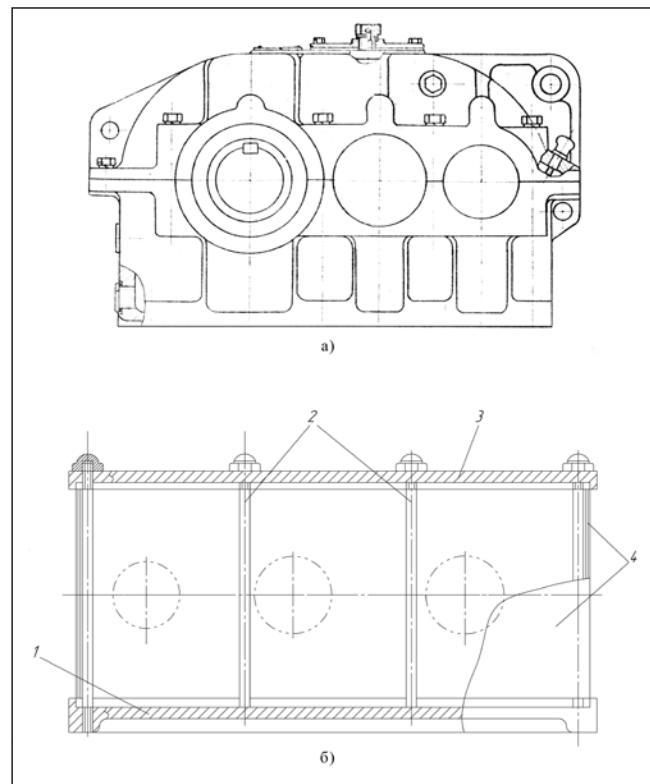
Корпус двухступенчатого редуктора: а) литой стандартный ВНИИРедуктор, б) навитой из ленты. 1 — основание, 2 — шпильки, 3 — крышка, 4 — многослойные стенки
